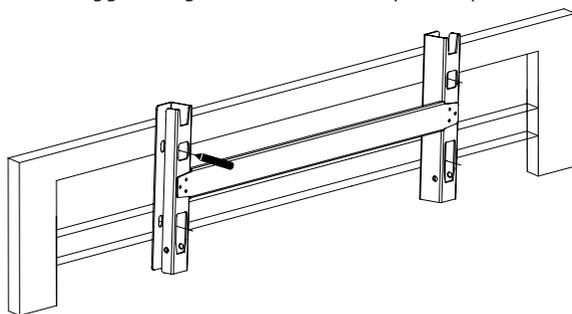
Segnare la posizione dei fori con la staffa di montaggio
